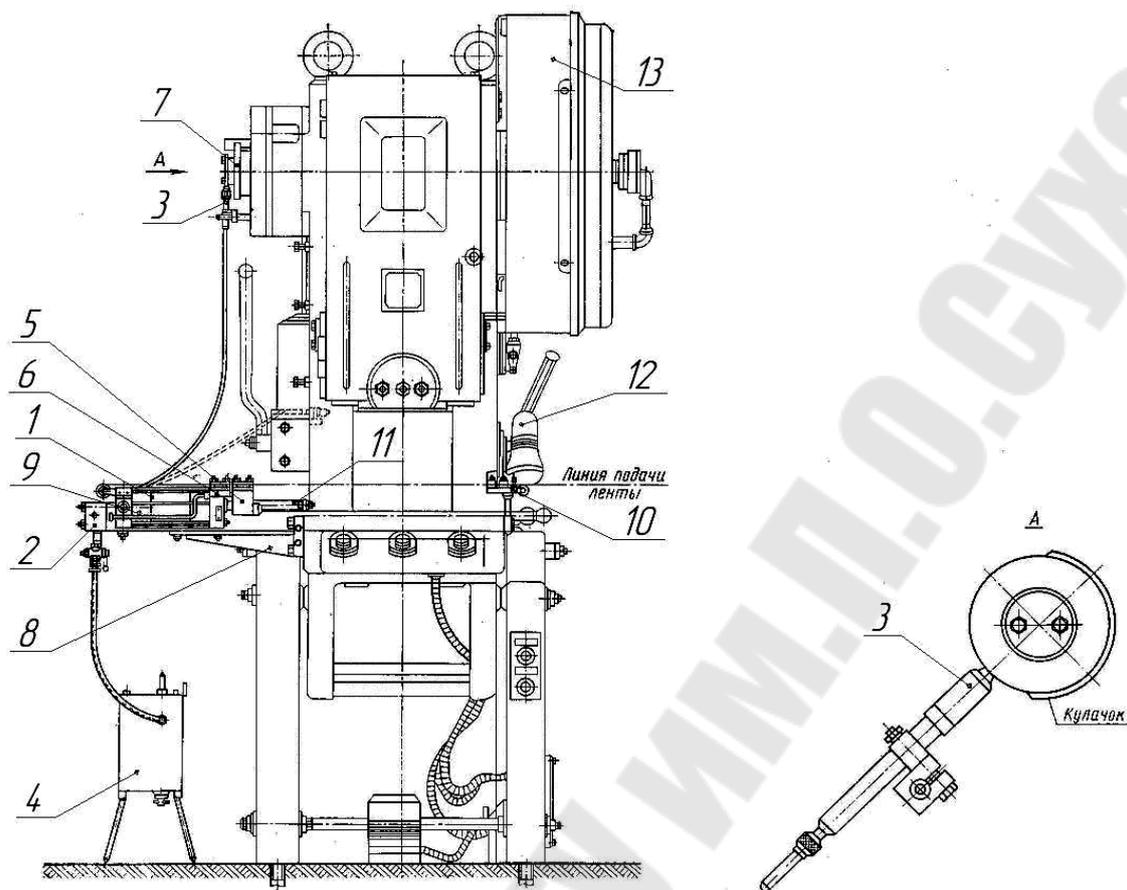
Общий вид клещевой подачи с прессом: 1 - подающее устройство, 2 - воздухораспределитель, 3 - клапан управления, 4 - узел подготовки воздуха, 5 - подвижная каретка, 6 - неподвижная каретка, 7 - кулачок, 8 - кронштейн, 9 - пневмоцилиндр, 10 - устройство для очистки и смазки ленты, 11 - цилиндрические направляющие, 12 - лампа, 13 - кожух маховика
